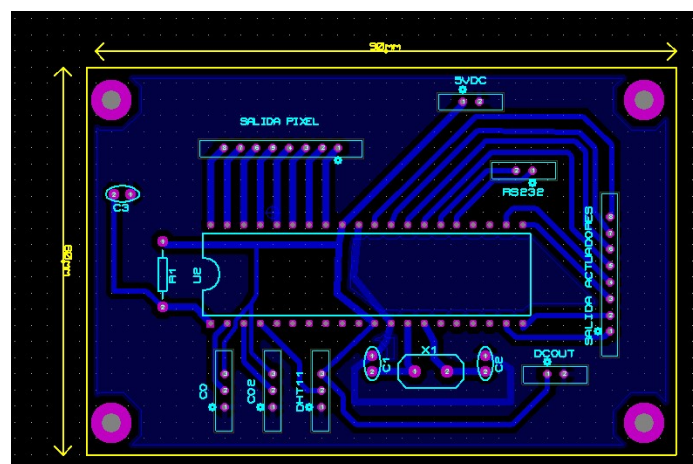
Diseño virtual del circuito PCB en Proteus ARES.
